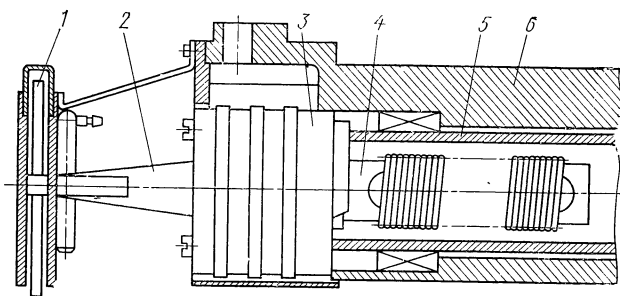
Акустическая головка сварочной машины МШУ-0,63
